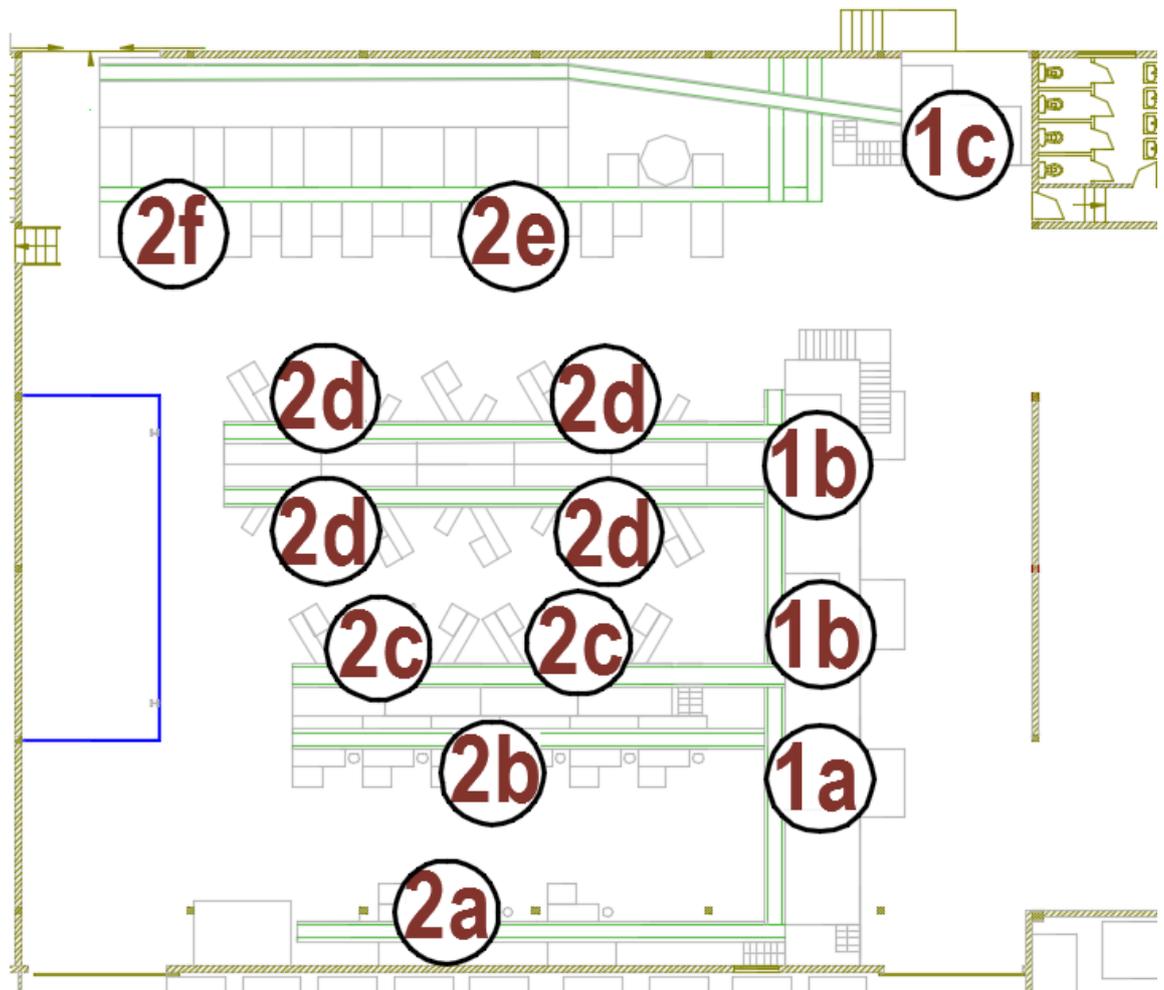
Planta atual da secção: Fabricação de Naturais
